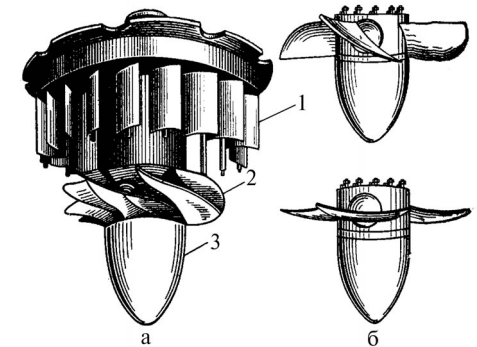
Поворотно-лопатєва турбіна: а - загальний вигляд; б - робоче колесо з відкритими лопатями (зверху) і закритими (внизу); 1 - напрямний апарат; 2 - поворотні лопаті; 3 - втулка з обтікачем.
